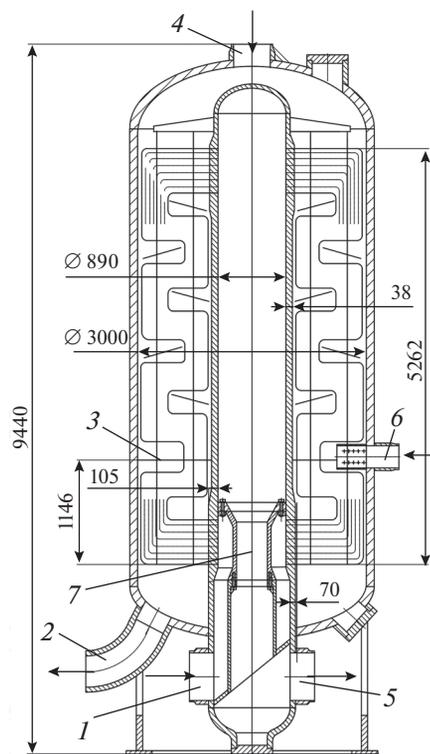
Подогреватель коллекторно-ширмового типа с трубным пучком из эвольвентных ширм в двухниточном исполнении (ПВД-Ш-5). 1–5 — см. рис. 1; 6 — вход конденсата; 7 — съемная вставка
